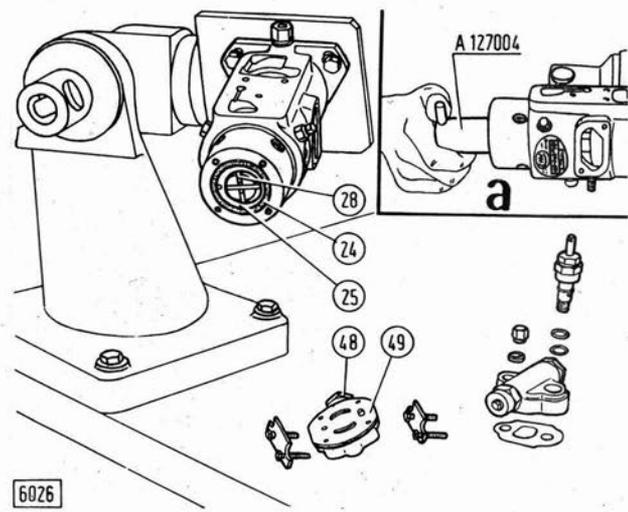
Vue de la pompe à palettes après dépose du couvercle de fermeture (49).
